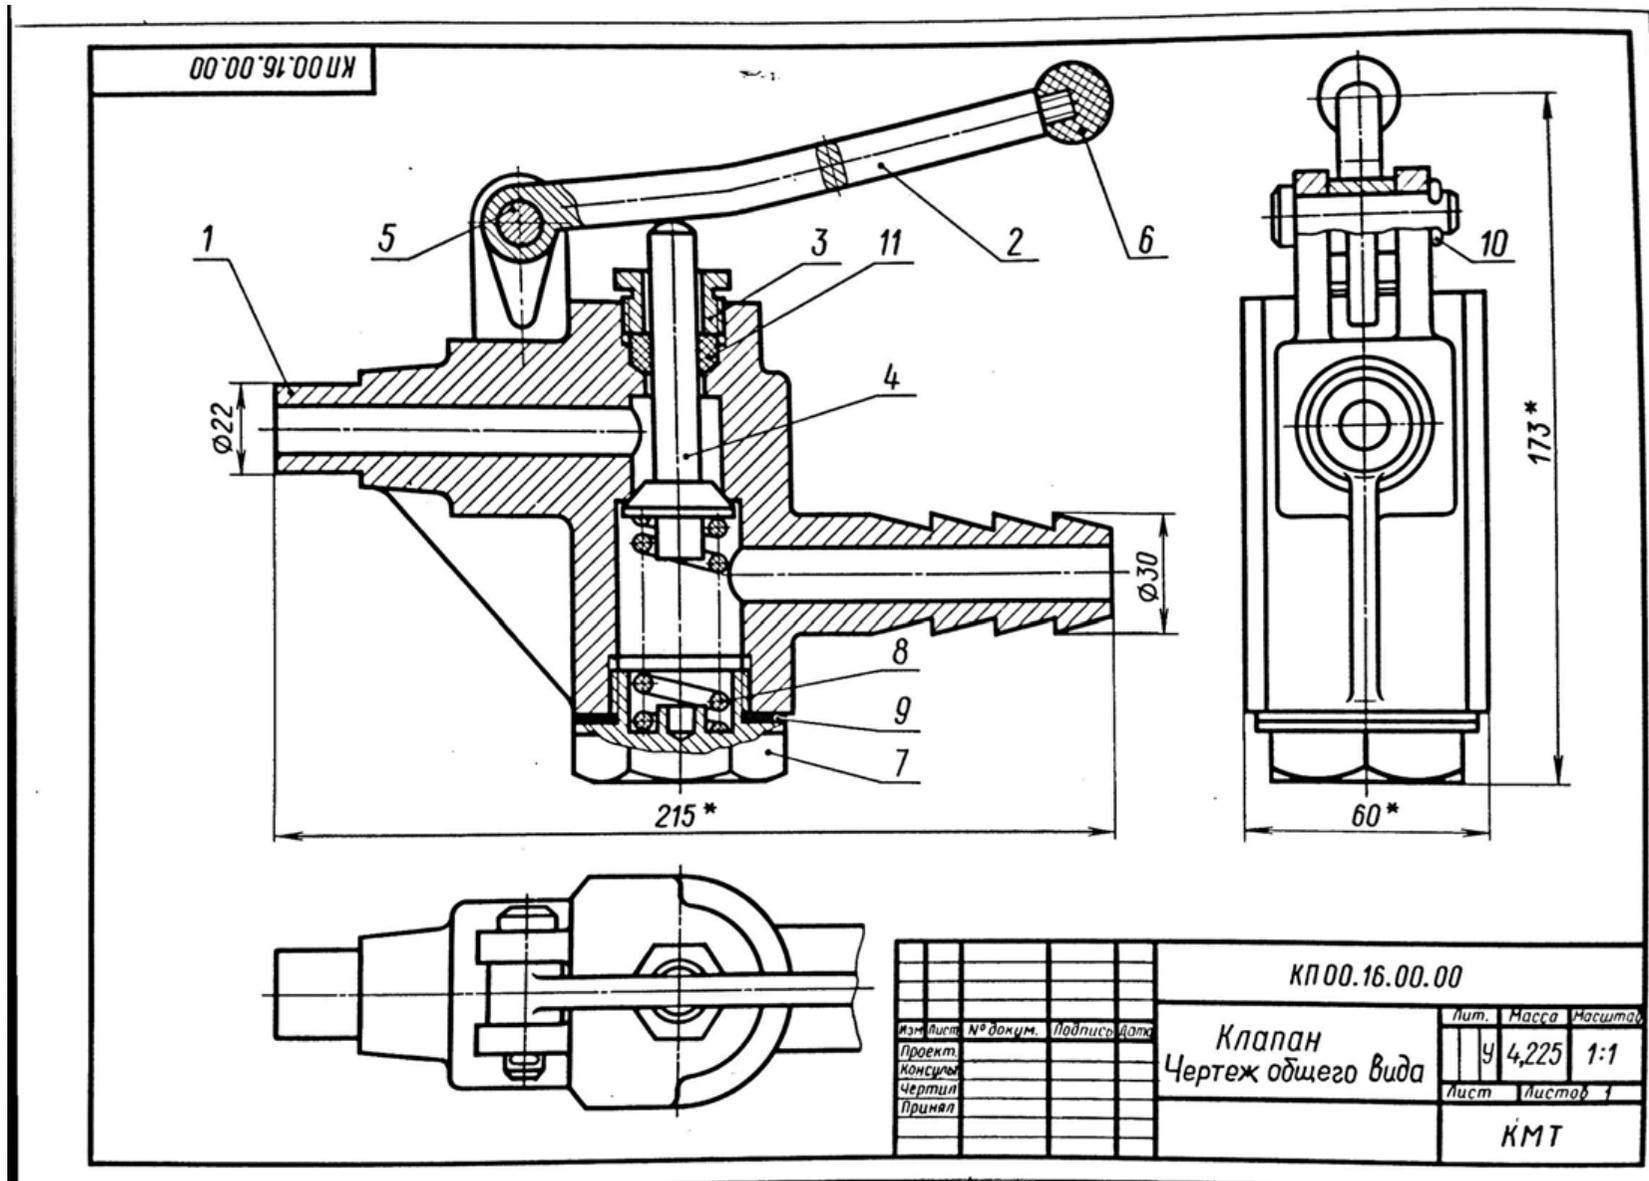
Сборочный чертеж клапана для обдувки отливок
